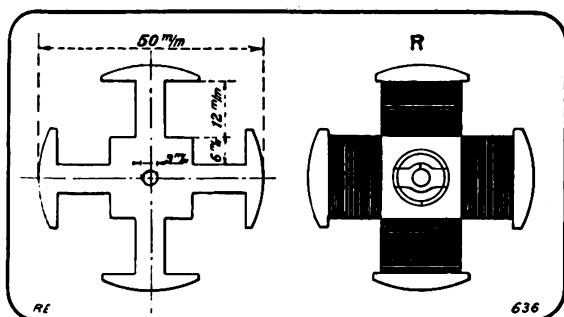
CONSTRUCTION DU ROTOR DU MOTEUR SYNCHRON. — A gauche, le découpage des tôles de 0,3 mm; à droite, le rotor assemblé.
